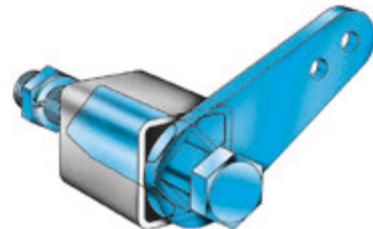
Innenvierkant aus Stahlrohr, Hebelarmbefestigung mittels durchgehender Schraube
